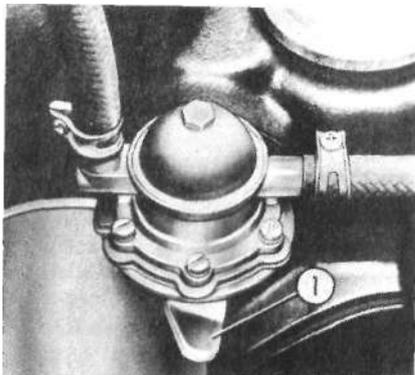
Топливный насос: 1 — рычаг ручной подкачки топлива
